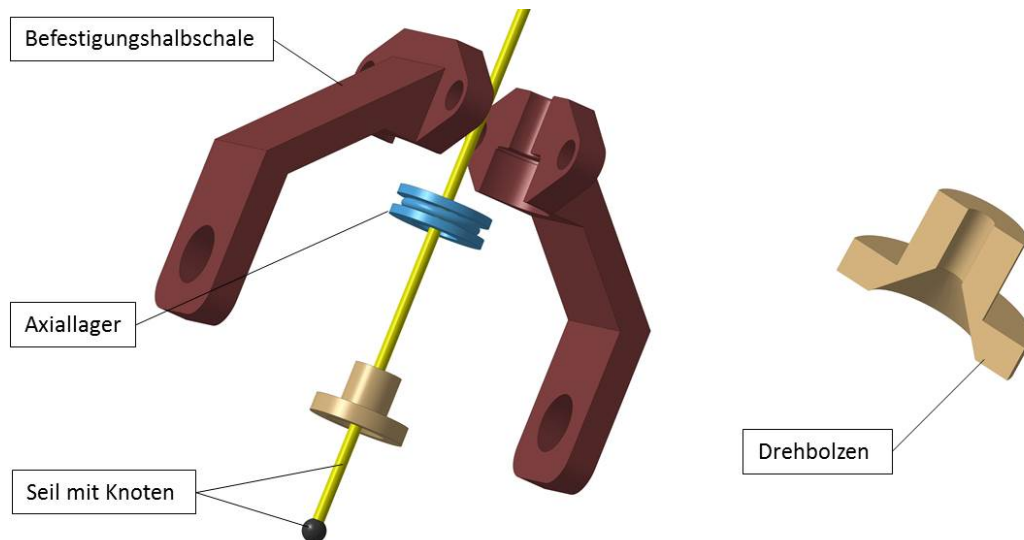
Prinzip der Befestigung (links); Drehbolzen im Schnitt (rechts)
